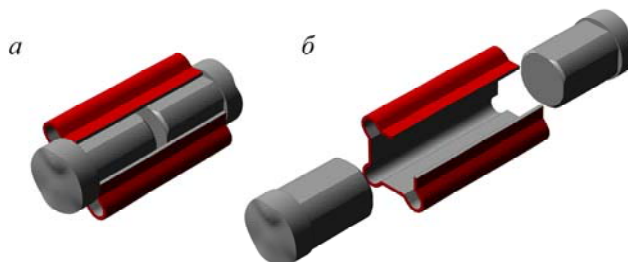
Модель муфти втулкової пружної: а – коли вали з'єднані; б – коли вали роз'єднані
